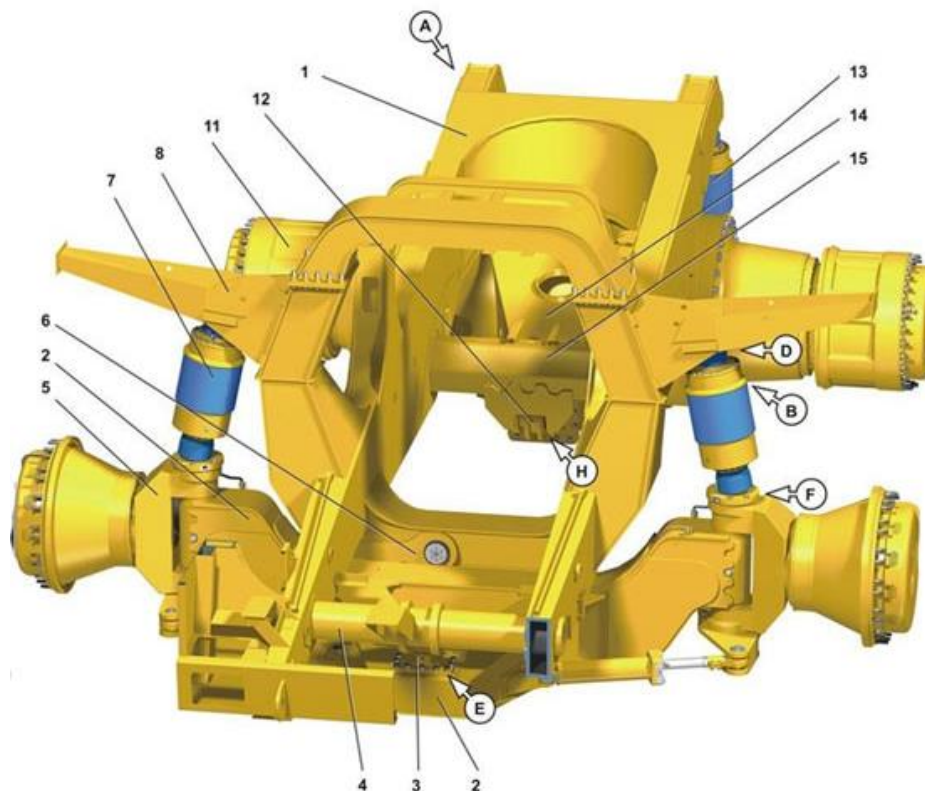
Внешний вид подвески БелАЗ 7530. 1 – рама; 2 – балка передней оси; 3 – шарнир центральный передней подвески; 4 – поперечина рамы; 5 – кулак поворотный; 6 – штанга поперечная передней подвески; 7 – ПГР подвески передней; 8 – кронштейн верхний крепления переднего цилиндра подвески; 9 – упор; 10 – упор; 11 – ограничитель поворота; 12 – мост задний; 13 – шарнир центральный задней подвески; 14 – ПГР подвески задней; 15 – рычаг заднего моста
